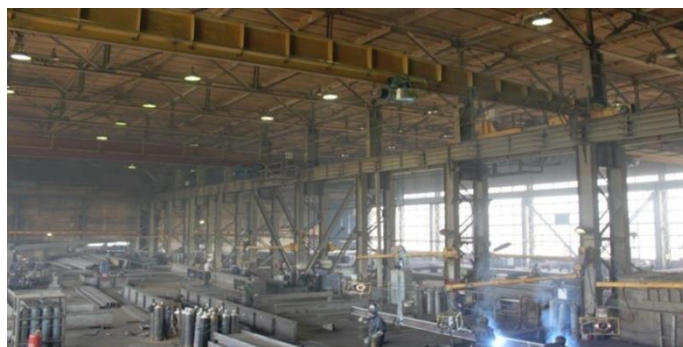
Складально-зварювальний цех по виготовленню різноманітних зварних конструкцій типу ферми
